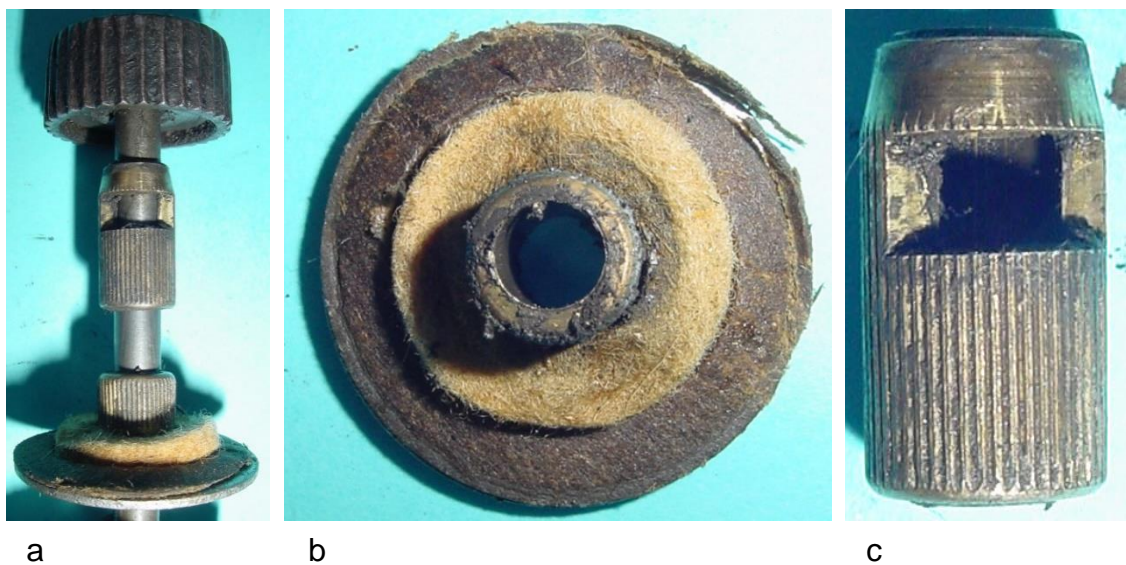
Lagerung: a) Welle mit zwei Gleitlagern, b) Unteres Lager mit Lagerschild und Filzring, c) Ölfenster im oberen Lager
